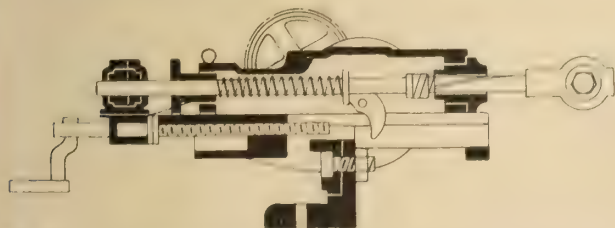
Schematischer Längsschnitt durch die Handstoßbohrmaschine der Jackson Drill Co.
